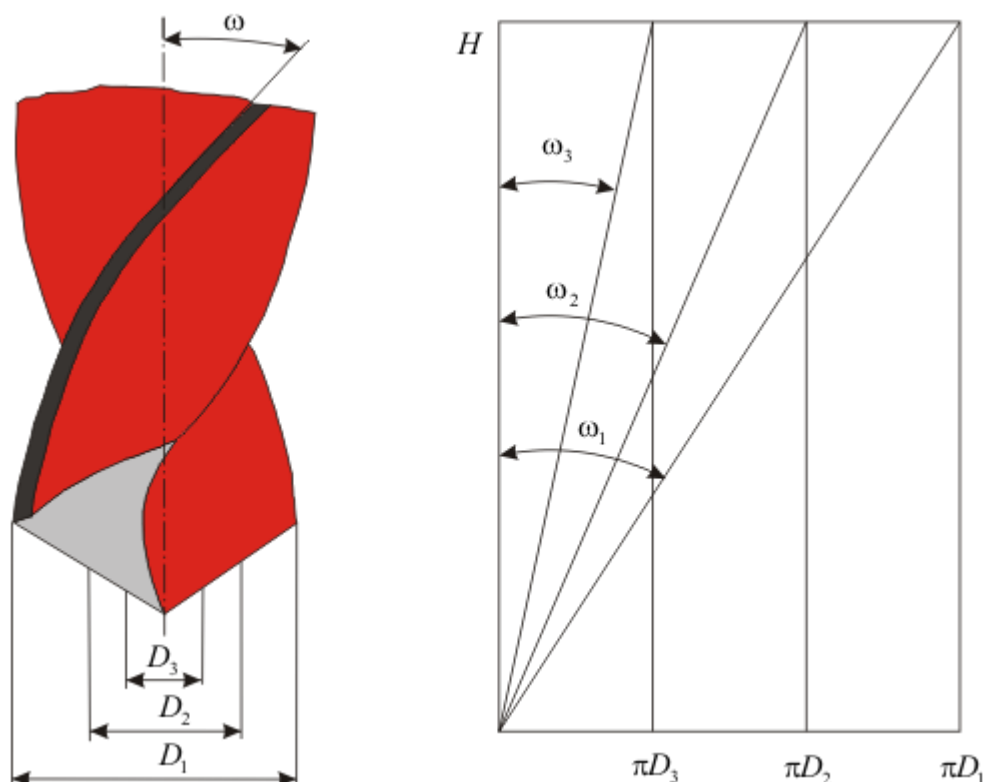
Измерение угла наклона винтовой канавки спирального сверла в цилиндрическом сечении
